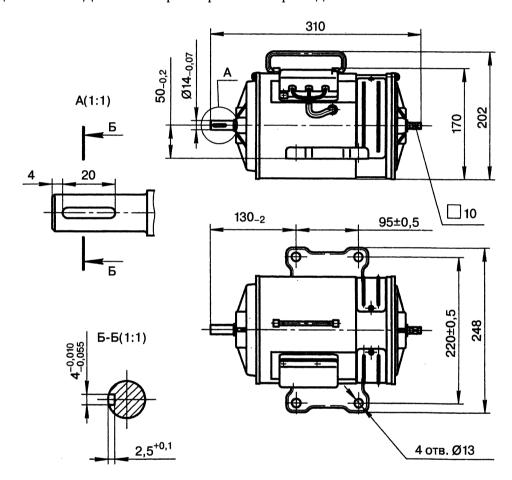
Габаритные, установочные, присоединительные размеры двигателей ДПС.
